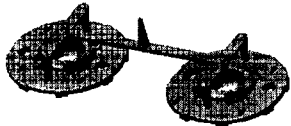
금형온도와 게이트 타입의 변화에 따른 Weld line 형상
